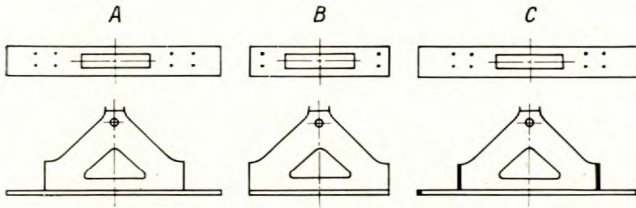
Bauformen des Stabeg-Universal-Tragelements TE 34.
